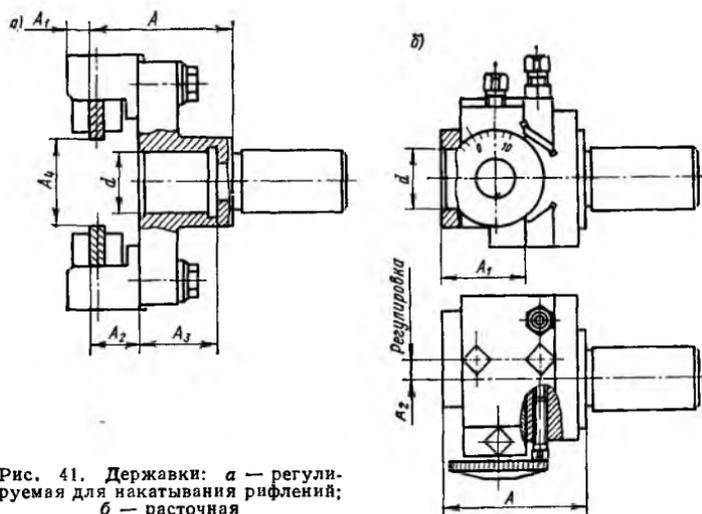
Державки: а — регулируемая для накатывания рифлений; б — расточная
